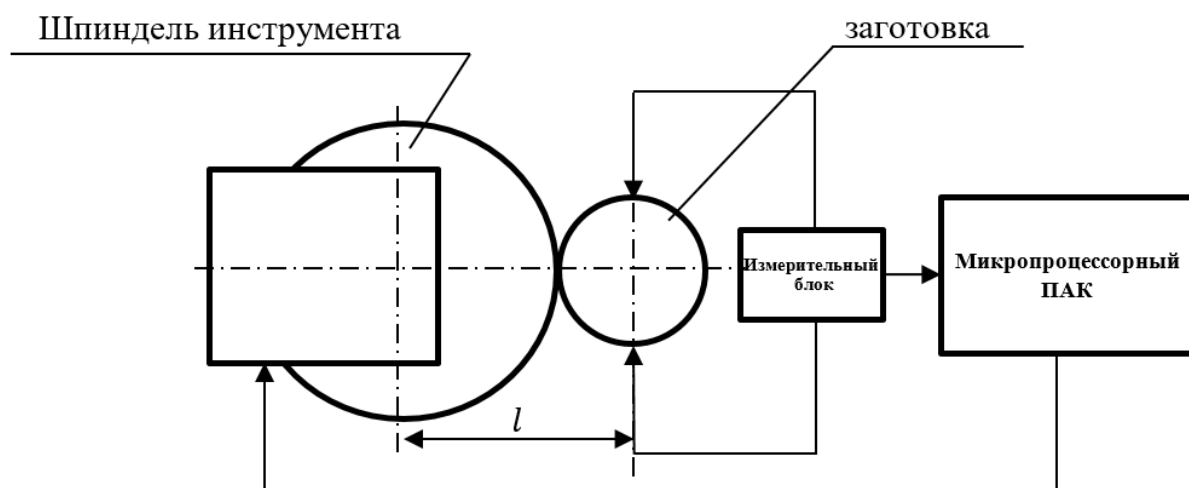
Общий вид схемы процесса обработки шлифованием.
